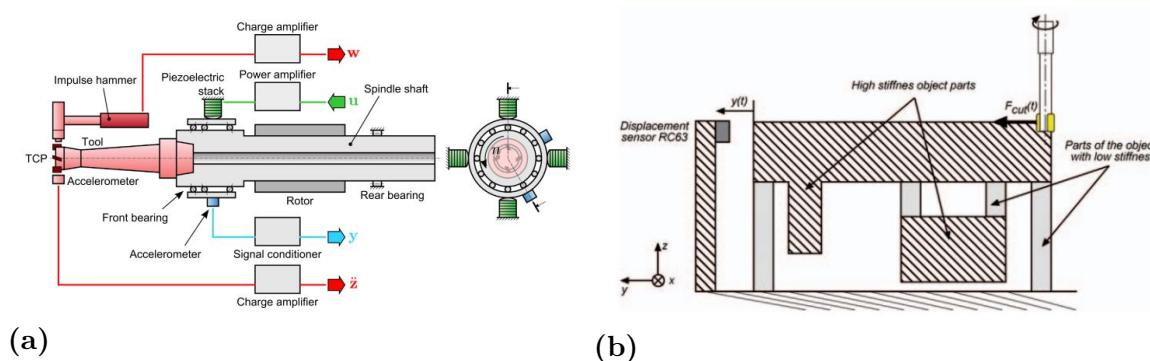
Dos opciones para el montaje de dispositivos activos para reducción de *chatter*. a) Montaje en la herramienta en (fuente [32]), b) montaje en la pieza a maquinar (fuente [35]).
